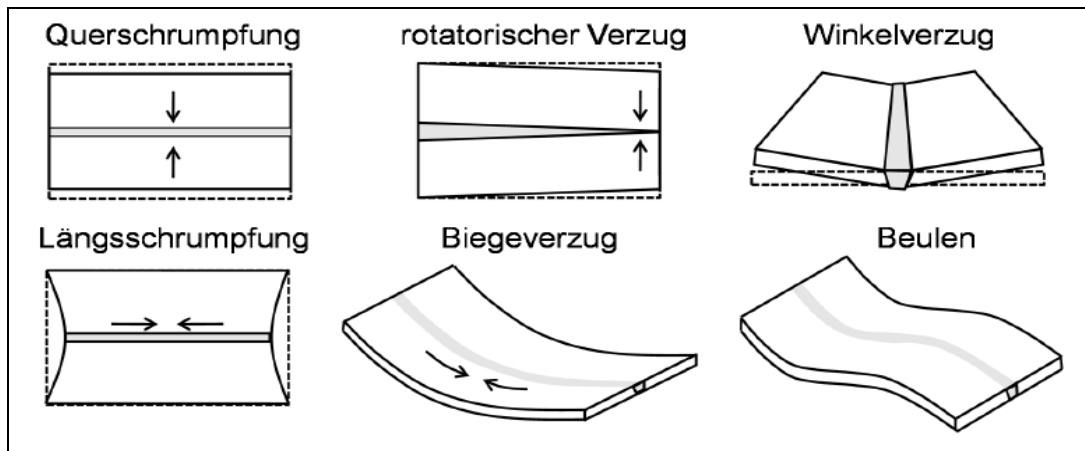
Grundlegende Schweißverzugsarten [3]
